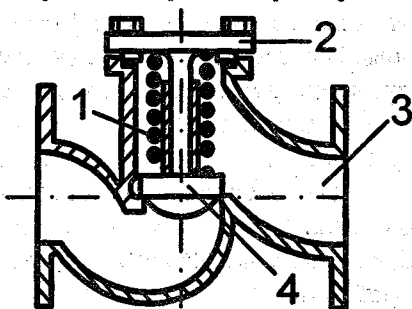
Обратный клапан: 1 – пружина; 2 – крышка; 3 – корпус; 4 – золотник
